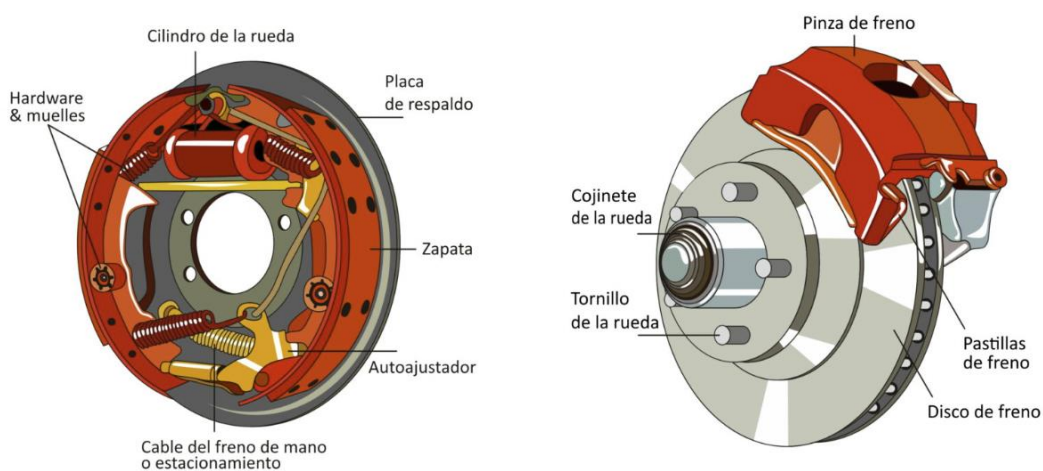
Partes freno de tambor (izquierda) Partes freno de disco (derecha) [18].
